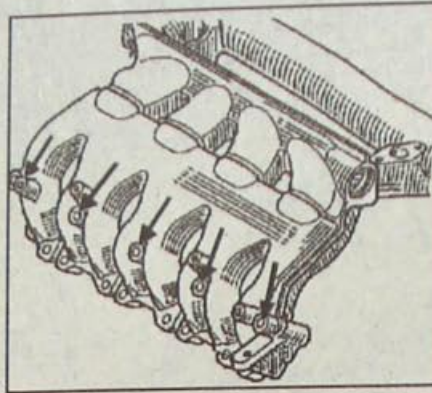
Расположение резьбовых шпилек крепления впускного коллектора
